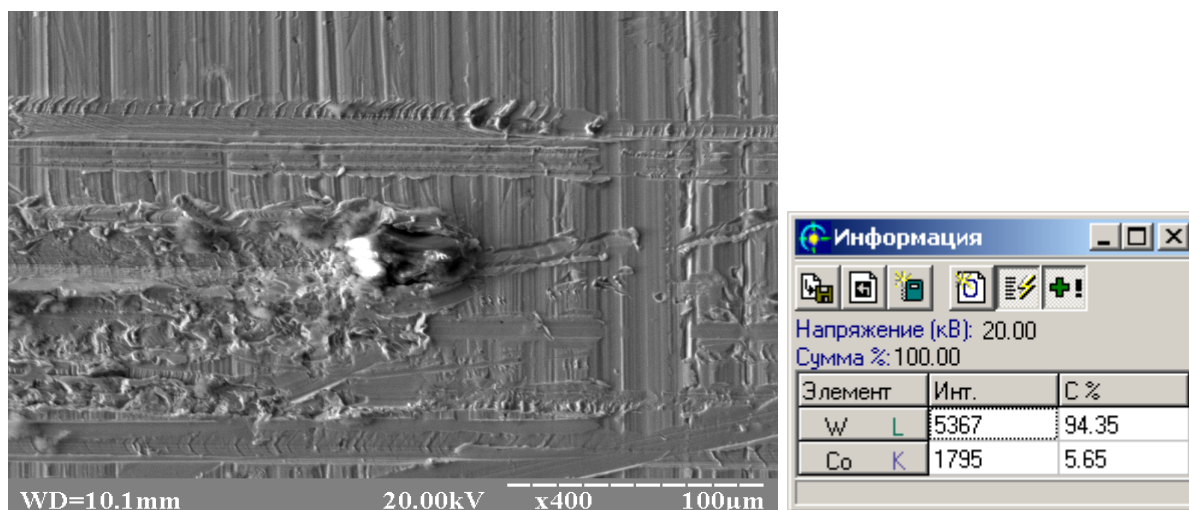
Повреждение поверхности золотника частицей твердосплавного инструмента
